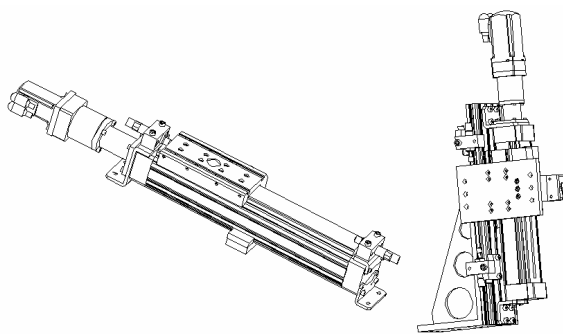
3 Krajní polohy manipulátoru před chladicí pecí
